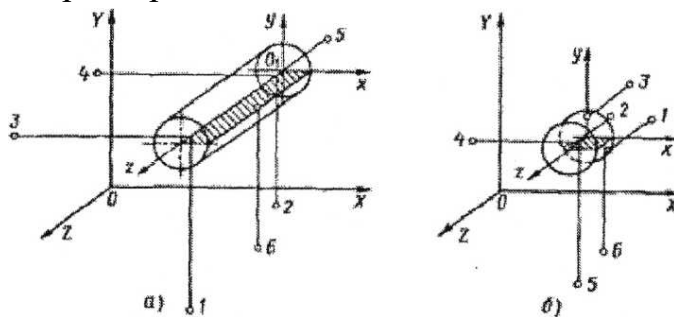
Схемы базирования деталей типа тел вращения: а - вал; б - диск
